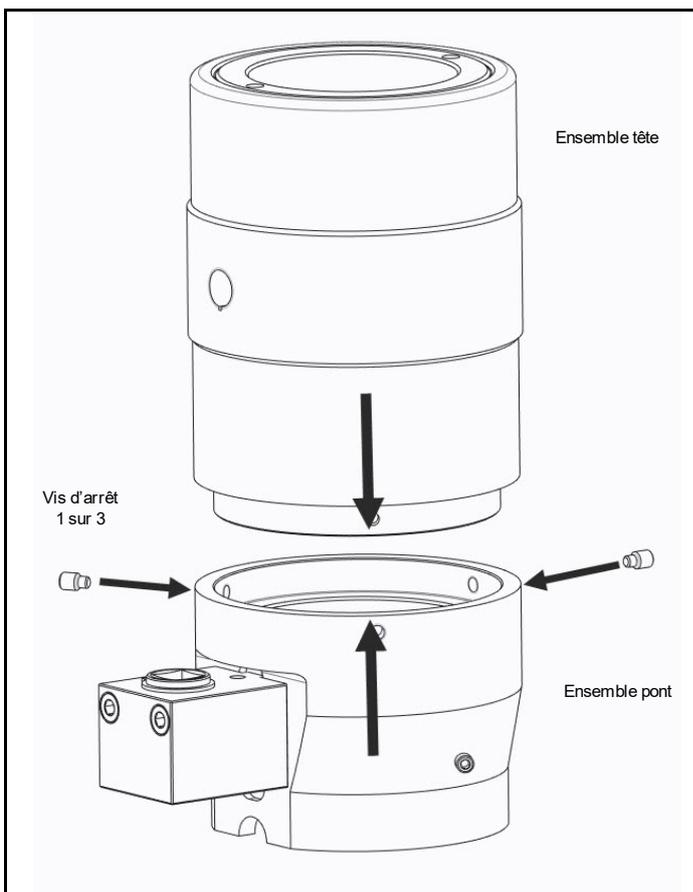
Placer l'ensemble tête sur l'ensemble pont; fixer avec des vis d'arrêt
